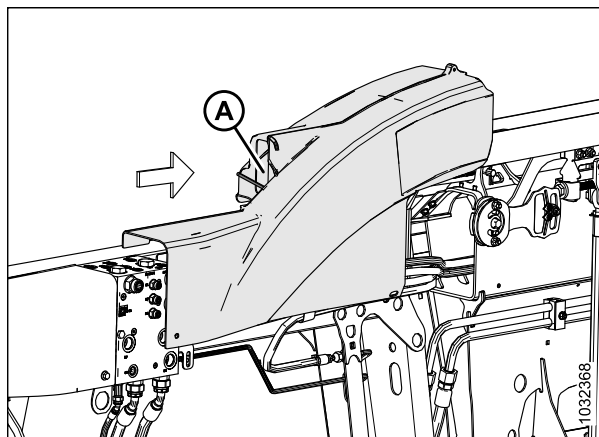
Левая крышка соединения — тыльная часть жатки
